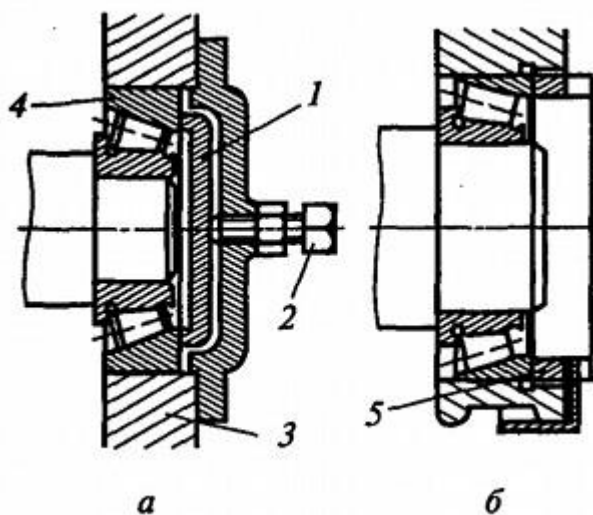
Схемы регулирования натяга конических роликоподшипников:
